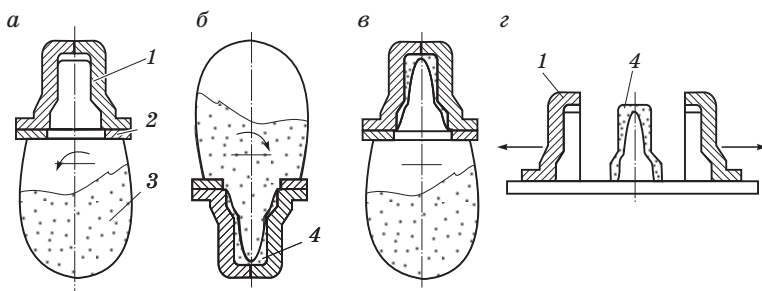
Схема бункерного изготовления оболочкового стержня
